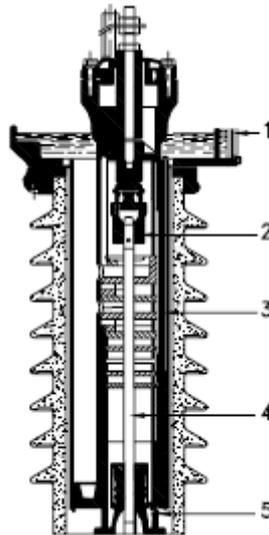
Cámara de extinción de un interruptor marca C.E.M.-Gardy, de pequeño volumen de aceite, de soplado mixto; 1.- Nivel de aceite, 2.- Contacto deslizante superior (fijo), 3.- Cubierta aislante, 4.- Espiga de contacto móvil, 5.- Contacto deslizante inferior (móvil).
